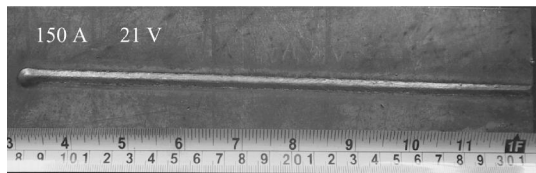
CO₂ 短路过渡焊接焊缝外面照片
